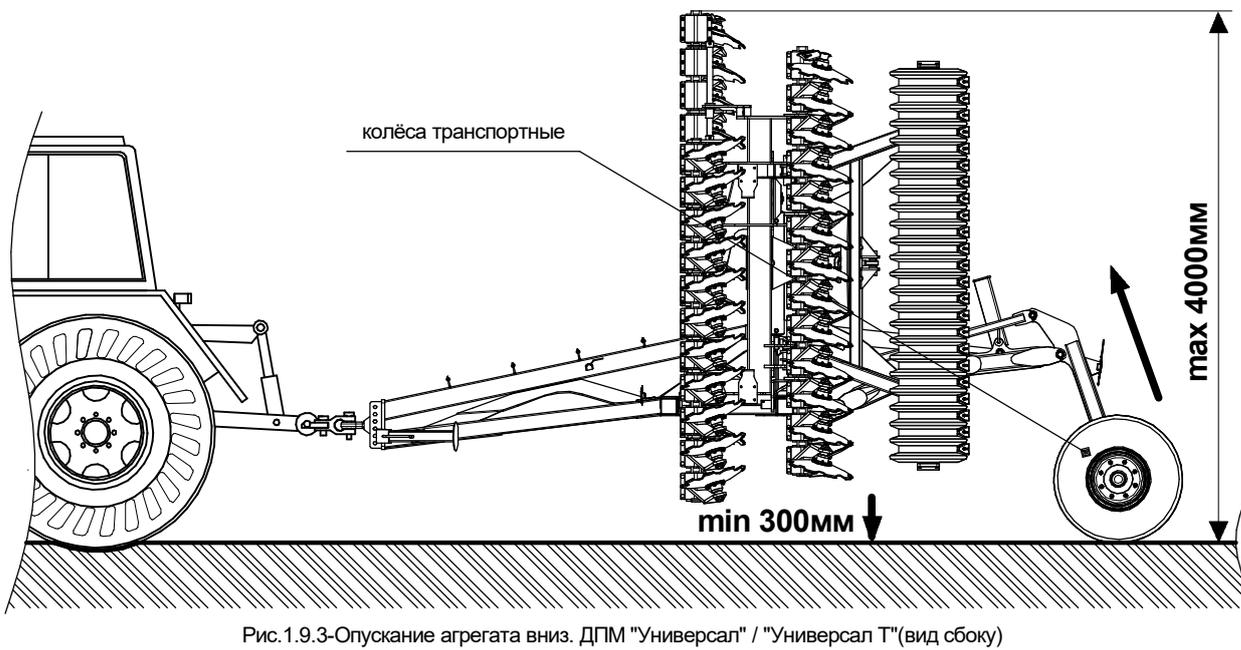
Опускание агрегата вниз. ДПМ "Универсал" / "Универсал Т" (вид сбоку)
